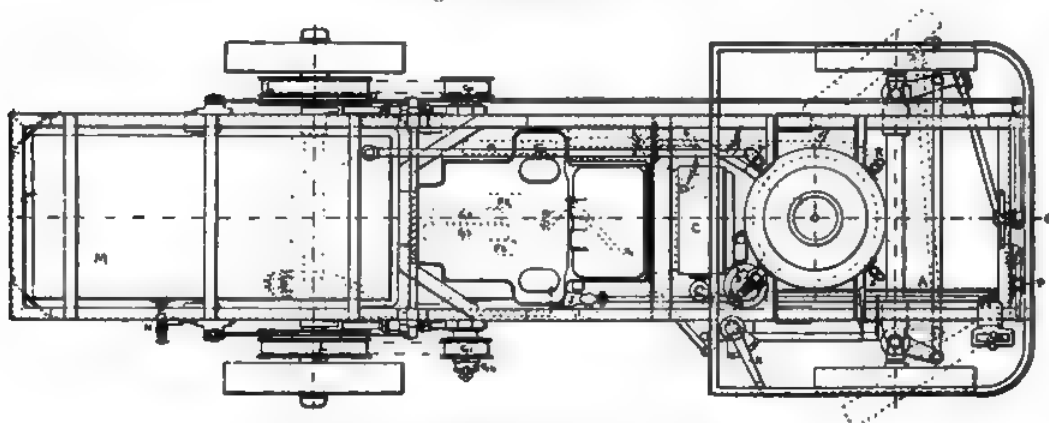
Grundriss des Coulthard'schen Dampf-Lastwagens.
